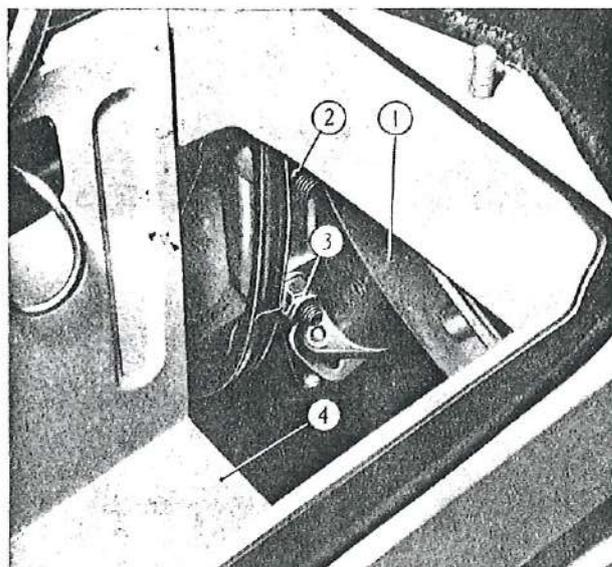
Detalle de la fijación de la caja de la dirección a la pared vertical del salpicadero.
